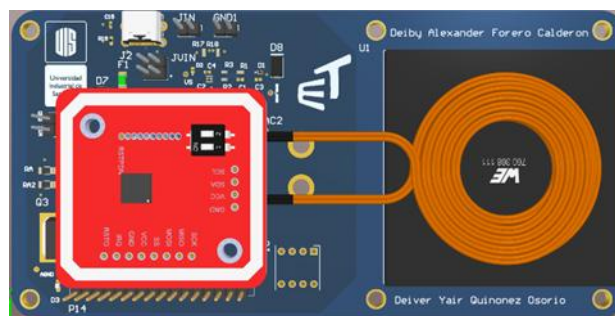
PCB final.*Figura D-8.*PCB final sin componentes.
